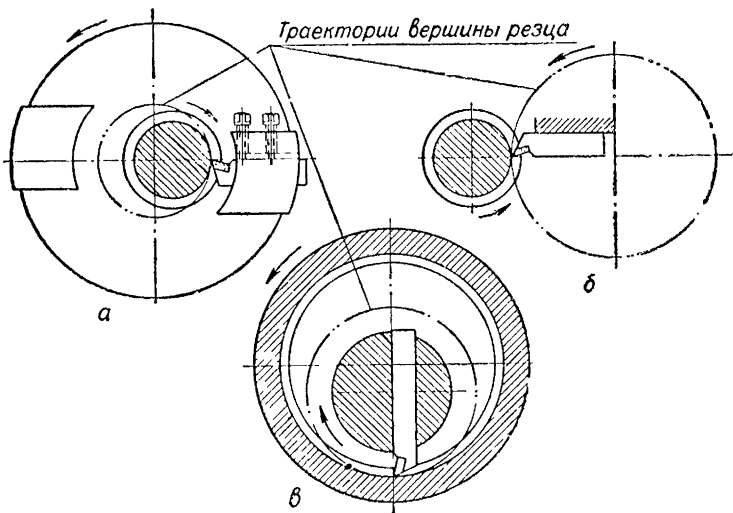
Схемы нарезания резьбы резцовыми головками: а — с внутренним касанием; б — с наружным касанием; в — нарезание внутренней резьбы.
